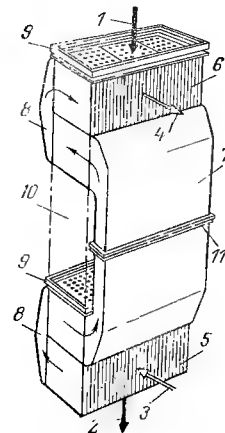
Трубчатый воздухоподогреватель двухъярусный.
